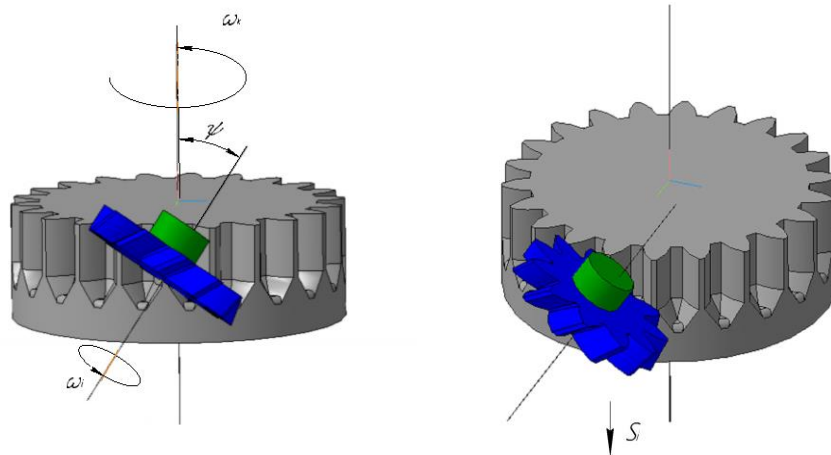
Схематичне розташування інструменту та заготовки під час обробки Power Skiving
